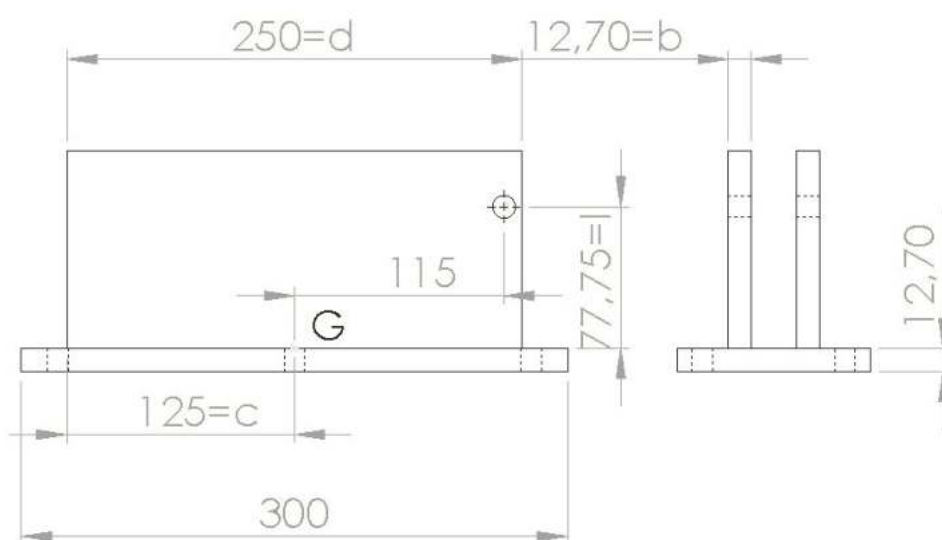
Vistas Monge del anclaje del motor, la letra G representa el centroide del cordón de soldadura.
